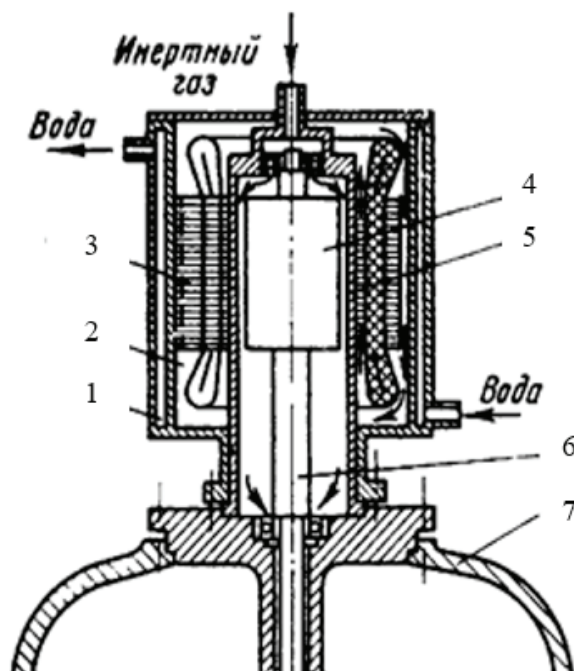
Схема герметичного привода: 1 — охлаждающая рубашка, 2 — масляная ванна, 3,4 — статор и ротор асинхронного электродвигателя, 5 — гильза экранирующая из немагнитного материала, 6 — вал, 7 — корпус реакционного аппарата
